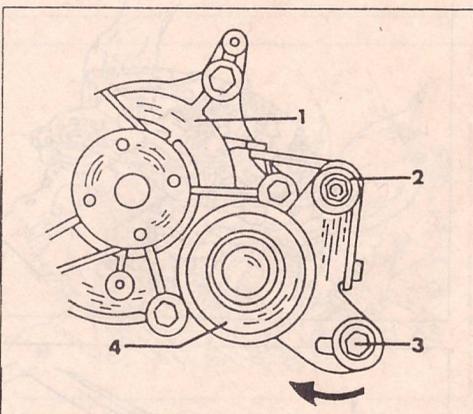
К снятию натяжителя зубчатого ремня у двигателей объемом 2,0 и 2,4 л.
